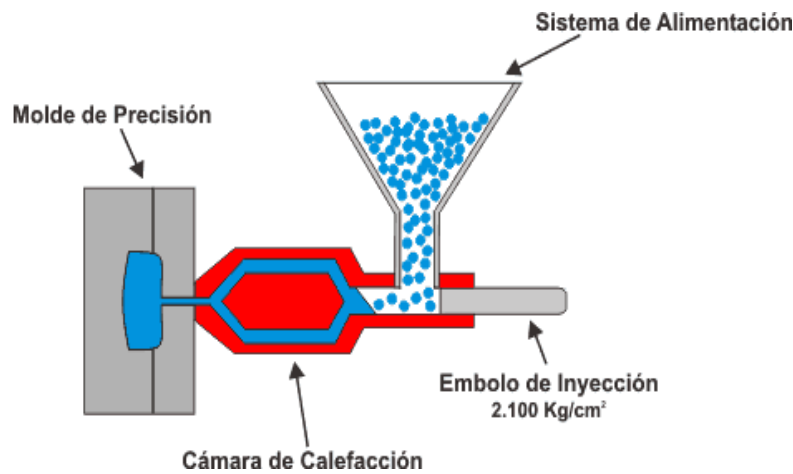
Esquema de un aparato de moldeo por inyección.
